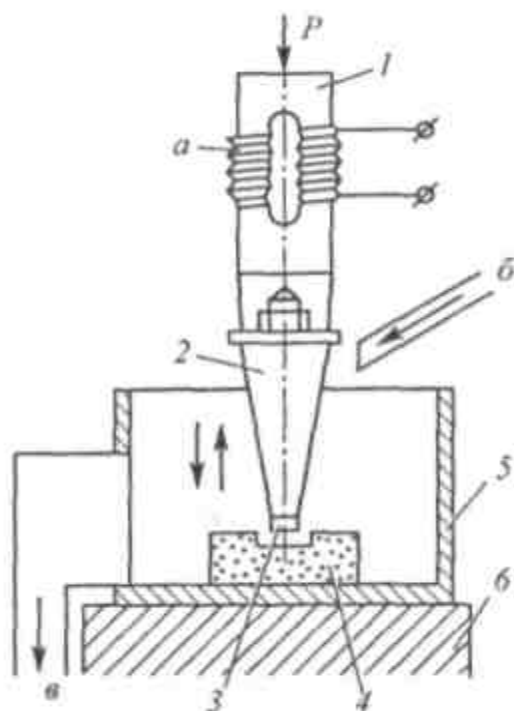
Схема процесса ультразвуковой обработки: 1 — магнито-стрикционный преобразователь; 2 — ванна; 3 — стол ультразвукового станка; 4 — заготовка; 5 — инструмент; б — концентратор; а — подвод тока от генератора; б — подвод абразивной суспензии; в — отвод продуктов процесса и суспензии; P — сила прижима инструмента к заготовке
